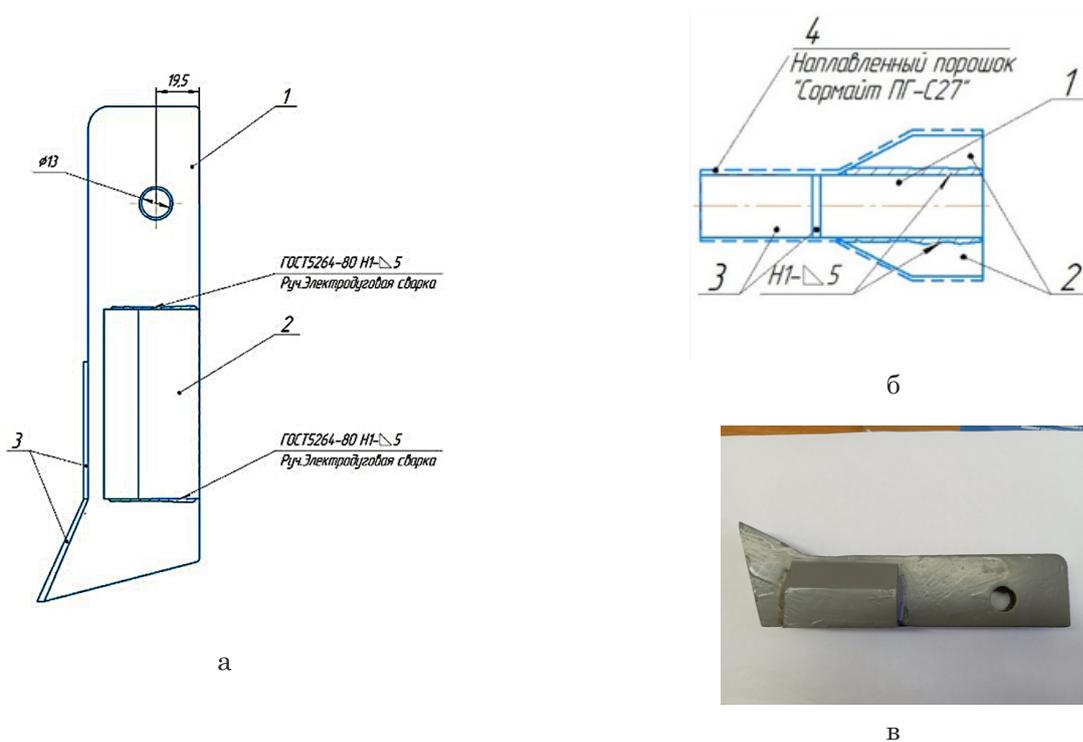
Сошник, изготовленный с помощью сварных швов:
